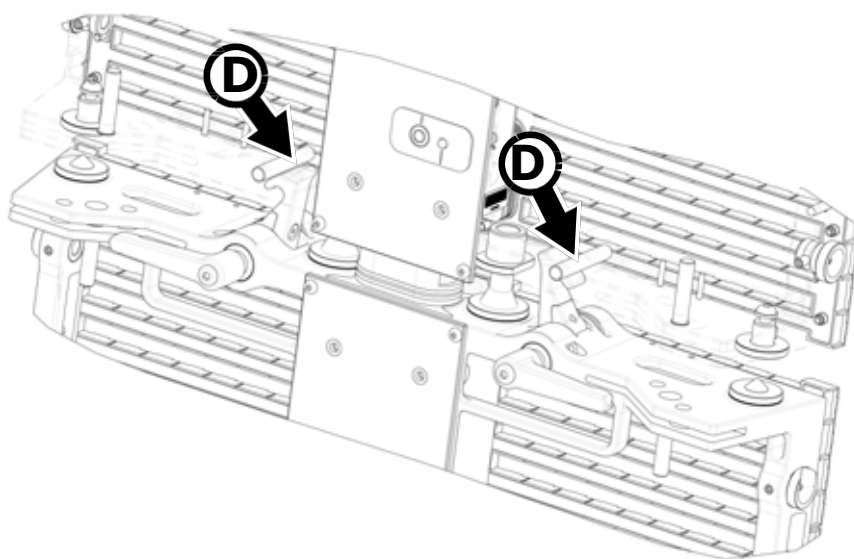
Непродвинутые крюки на штырях блокировки (вид в разрезе)
